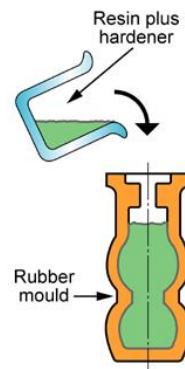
Esquema do Processo de moldação por fundição("CES EduPack 2014").
